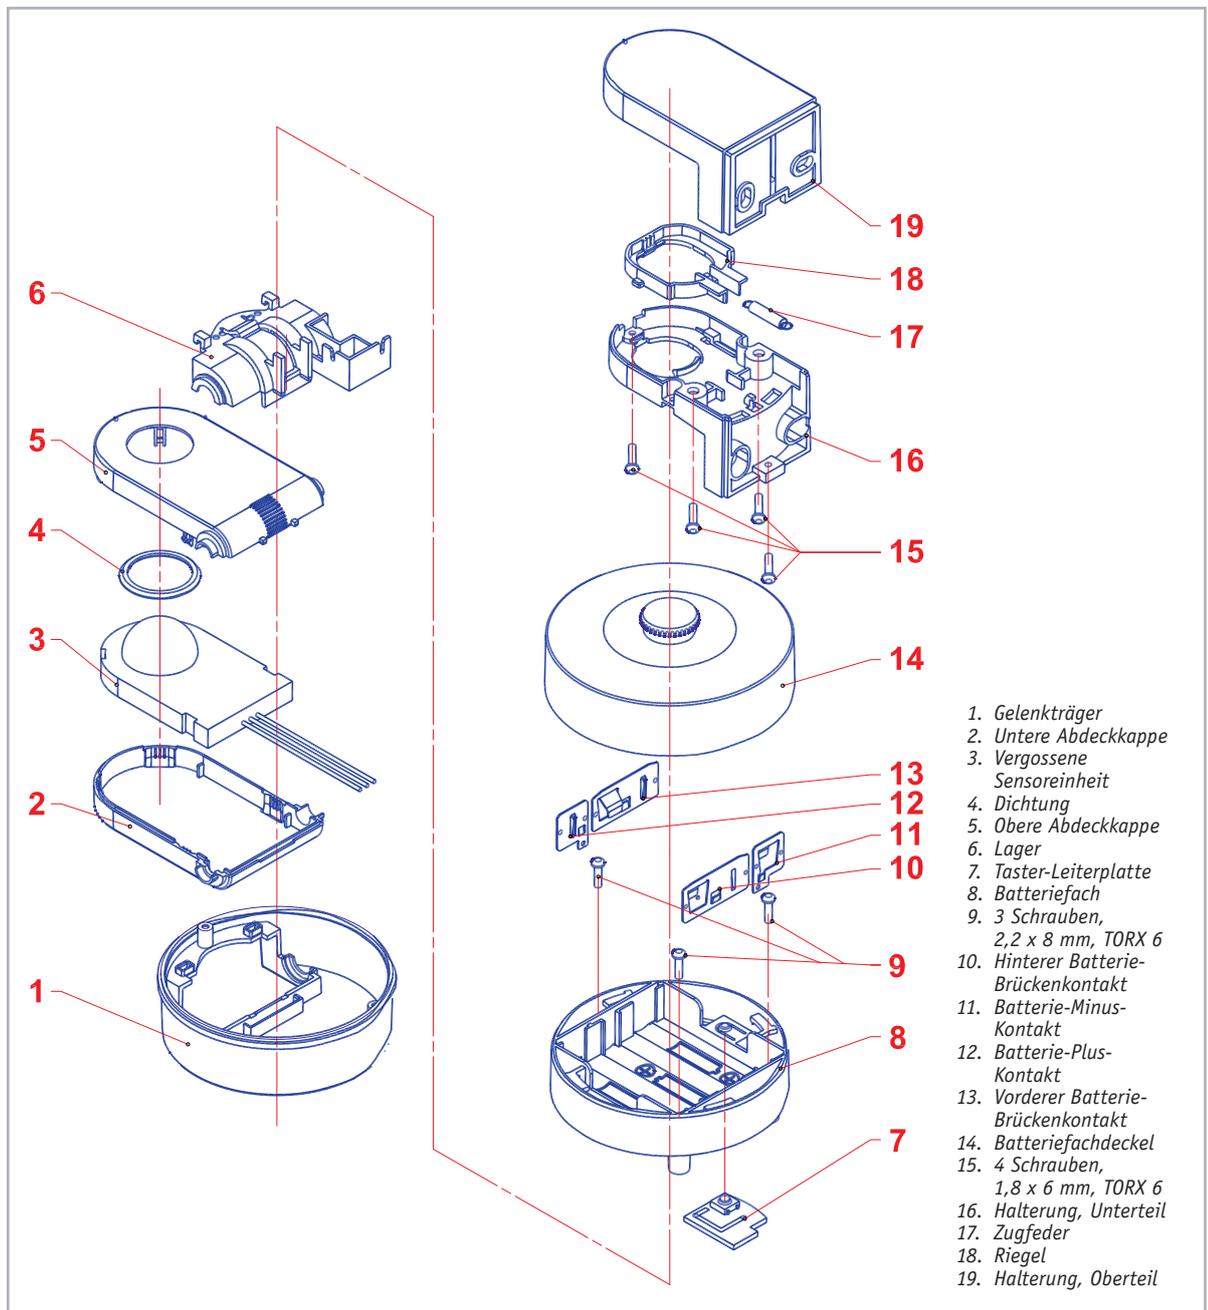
Die Explosionszeichnung gibt einen Überblick über den mechanischen Aufbau.
